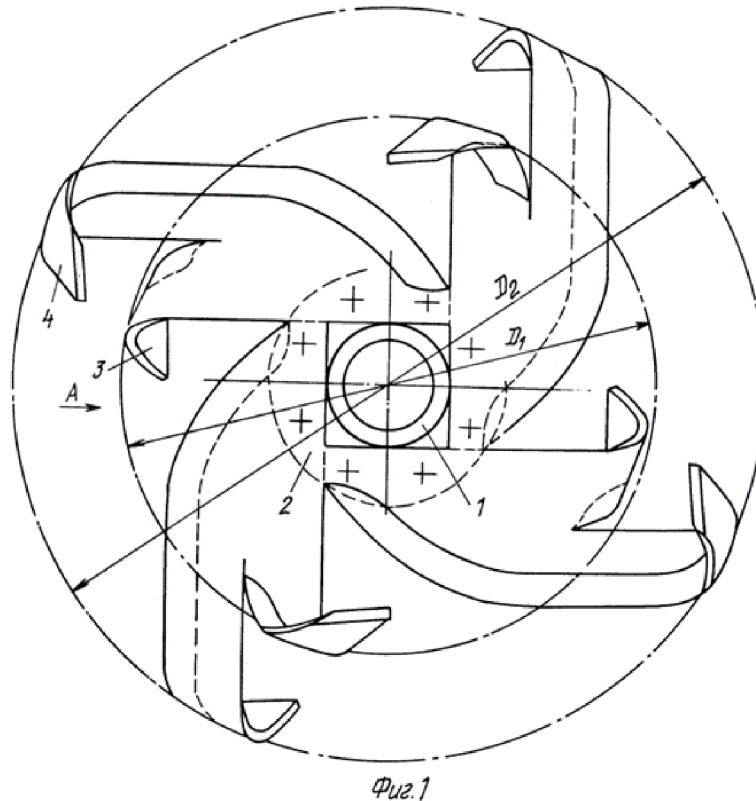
Рабочий орган фрезы с разновеликими ножами.
